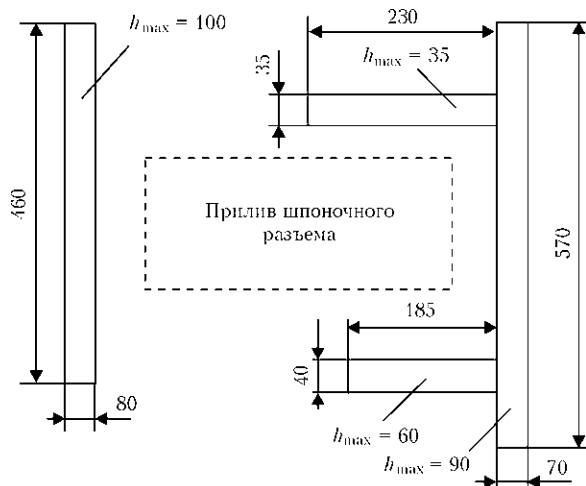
Схема расположения выборок трещин на внутренней поверхности крышки корпуса ЦВД турбины К-300-240 ( $h$  — глубина выборки)
